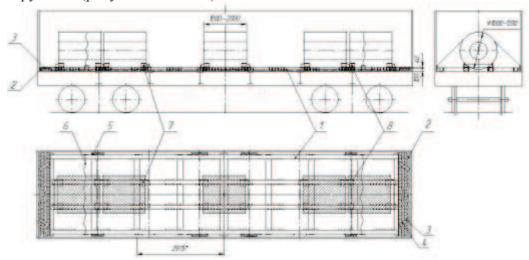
1-рама; 2-упорный брусок; 3-скрепляющая доска; 4-гвоздь; 5-распорный брусок; 6-увязка; 7, 8-упор
